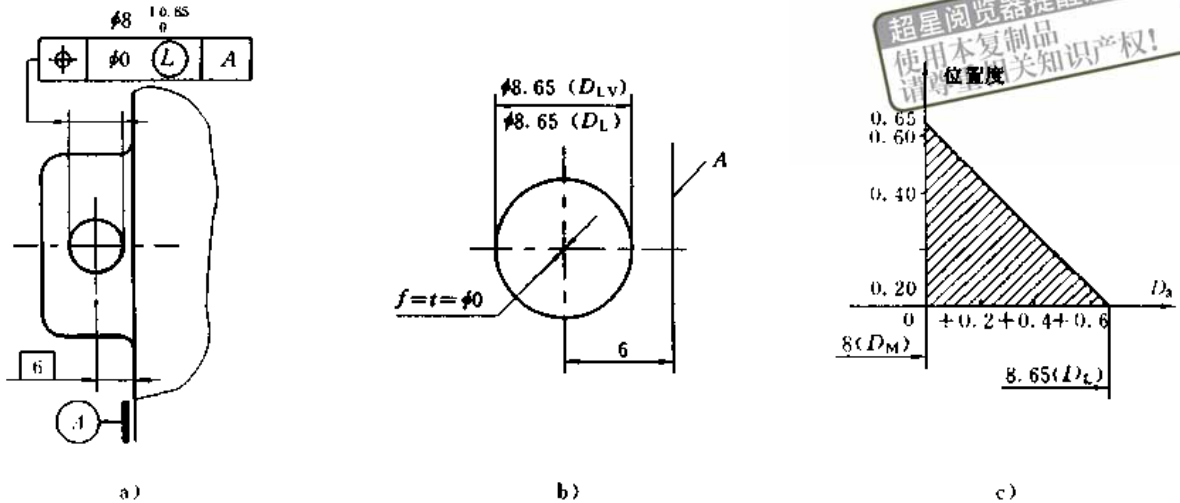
轴线位置度公差采用最小实体要求的零形位公差
